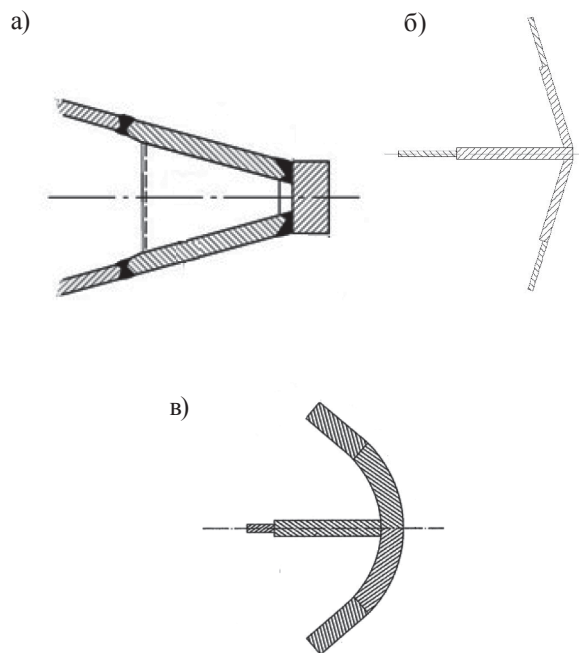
Сварной форштевень: *а* — брусковый сварной форштевень с острыми кромками;
